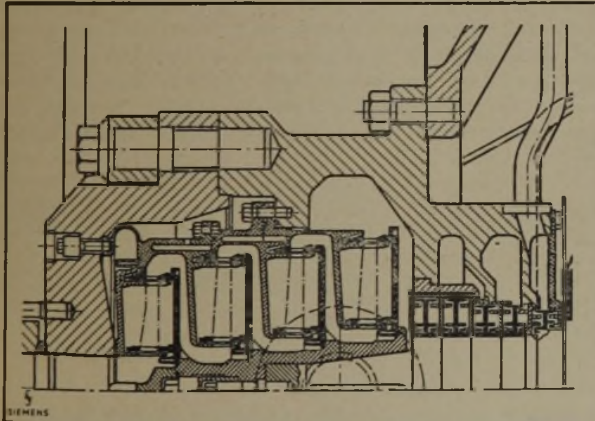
Höchst-Druckzylinder einer Gegendruckturbine, Bauart Siemens-Meininghaus (Werkfoto SSW)
